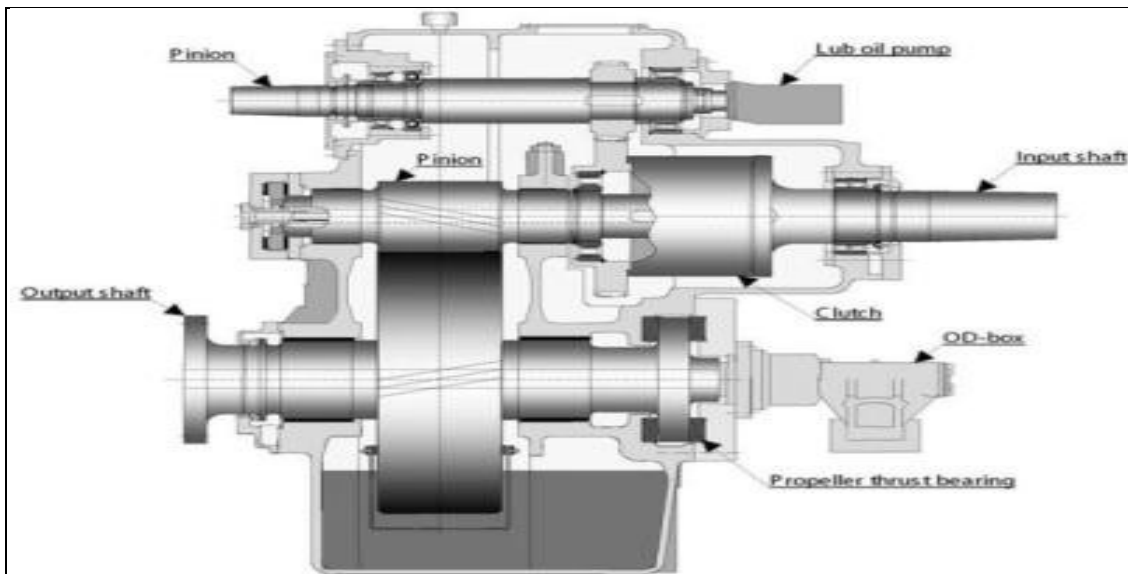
Σύστημα λίπανσης και ψύξης [*Michell Bearings hydrodynamic propeller shaft bearing and thrust block - YouTube*]
